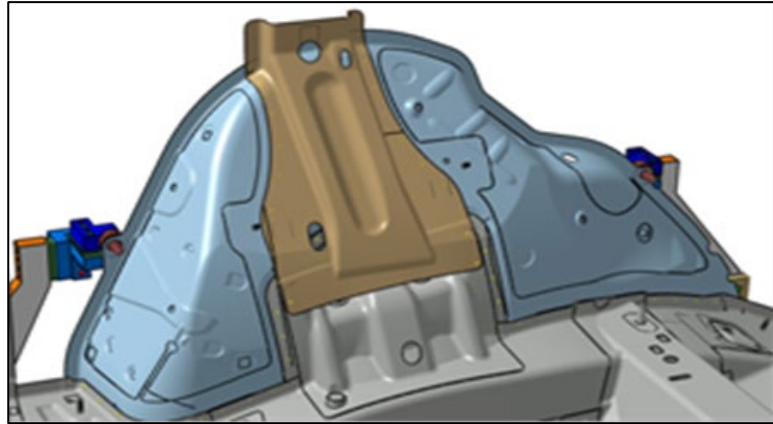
Posicionamiento del refuerzo de bomba trasera izquierda.
